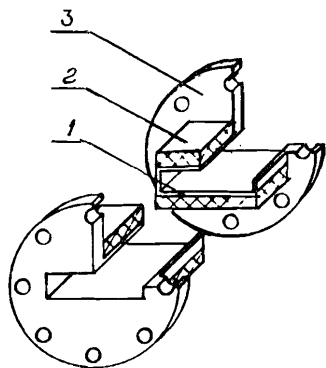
Внешний вид насоса. 1 – корпус, 2 – магнит, 3 – фланец.
